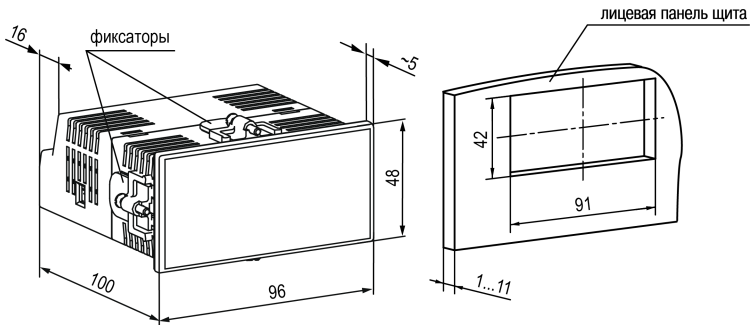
Габаритные размеры корпуса Щ2 и монтажного отверстия в щите
